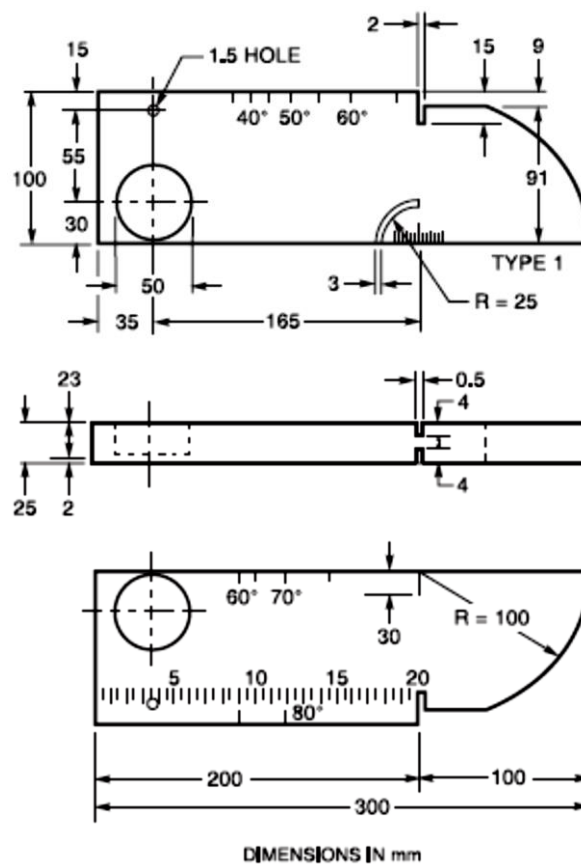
BLOQUE DE REFERENCIA DEL INSTITUTO INTERNACIONAL DE SOLDADURA (1)
